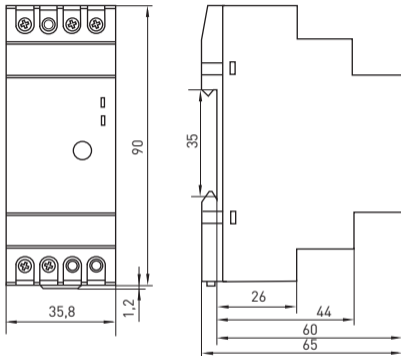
Габаритные размеры фотореле DIN-1 (ФР)
